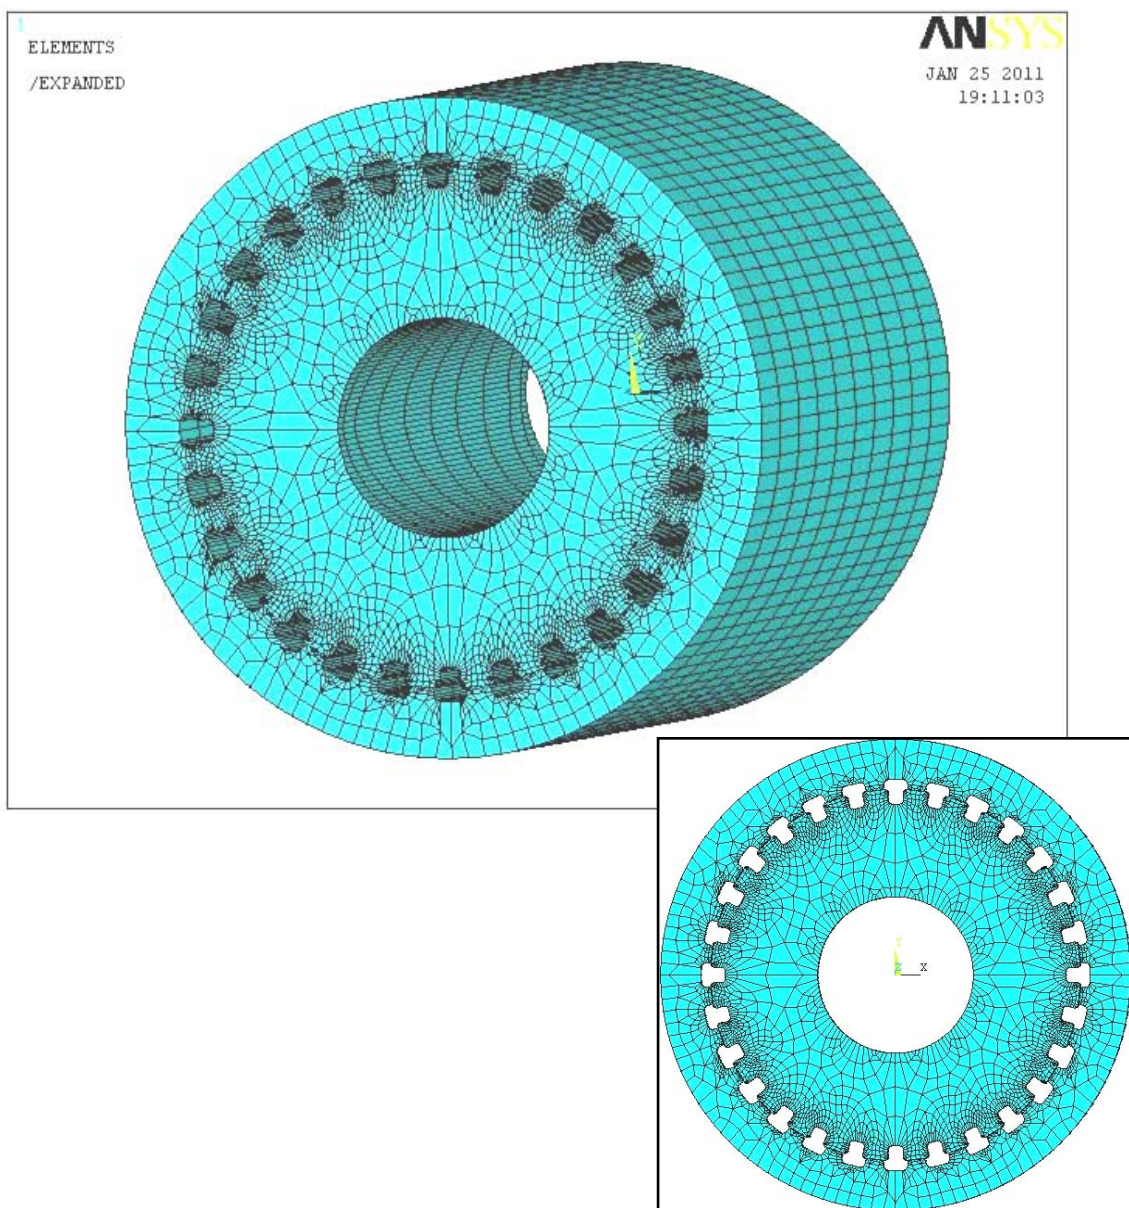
Immagine del modello solido dell'albero accoppiato con la camicia e vista frontale dell'assemblato, dotati di mesh.
